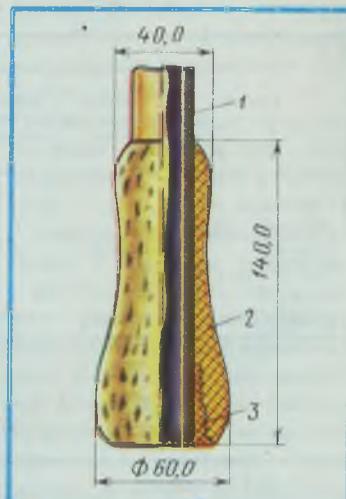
Надставка: 1 — комель удлинителя; 2 — надставка; 3 — пробка колма.
